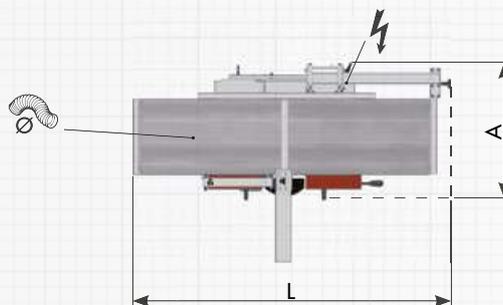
Foto simbólica de A3 26, A3 31, A3 41, A3 41A
